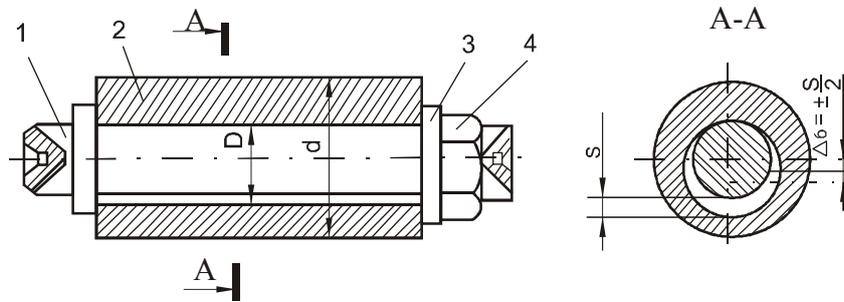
Схема образования погрешности базирования при установке заготовки на цилиндрической оправке с зазором: s – зазор; Δ_b – погрешность базирования; 1 – центровая цилиндрическая оправка; 2 – заготовка (штулка); 3 – быстросменная шайба; 4 – гайка
